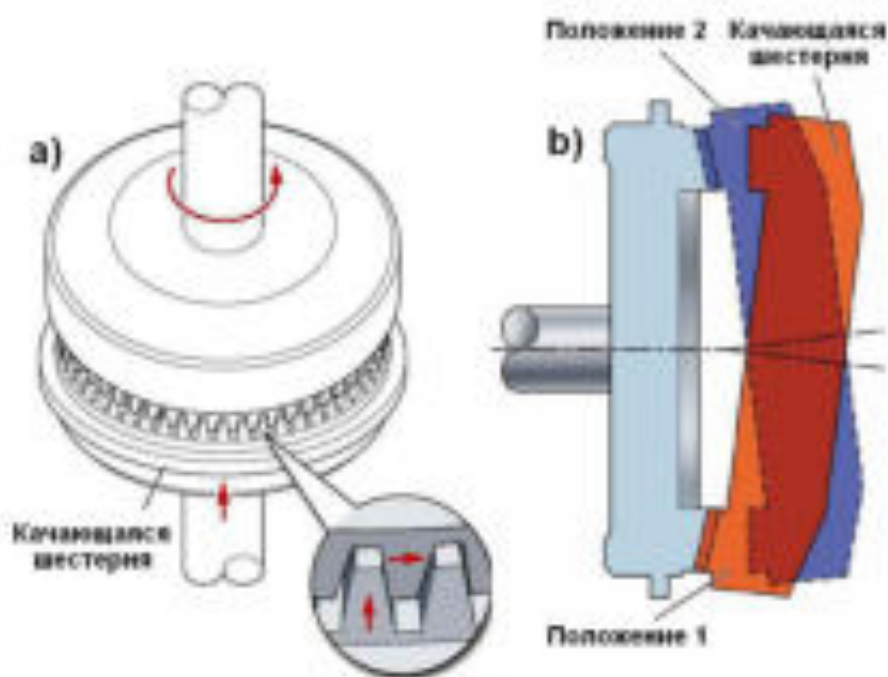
Работа качающейся шестерни редуктора привода стояночного тормоза с электрическим управлением.
